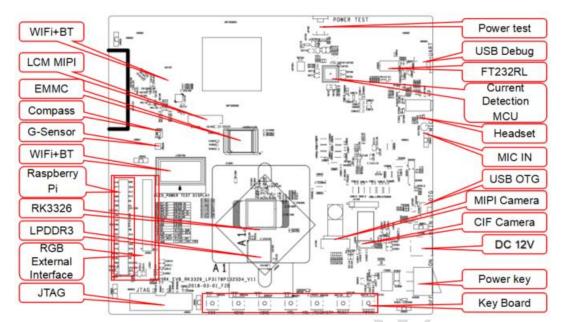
RK3326 EVB 1.1 PCB上TOP Layer模块布局位置图
